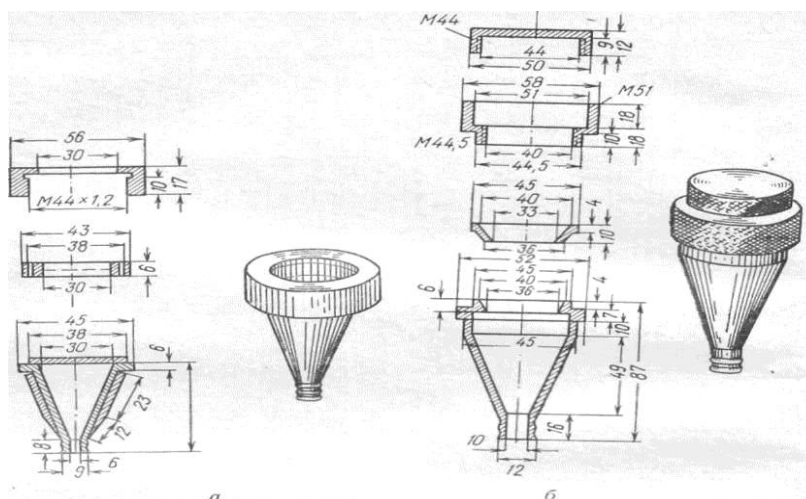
Патроны для отбора проб пыли на фильтры: а-пластмассовый; б- металлический
